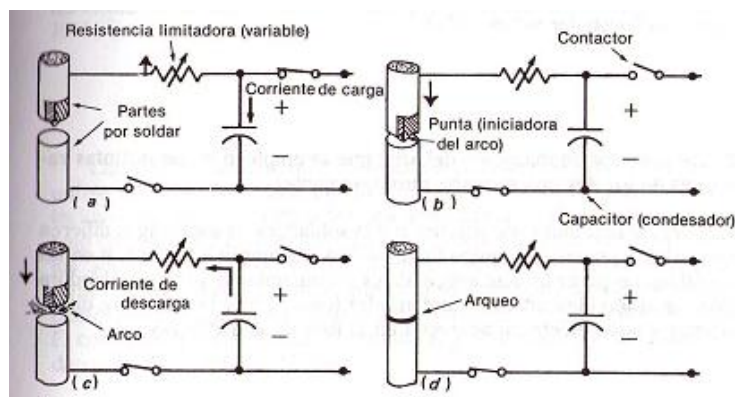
Diagrama simplificado de la secuencia de pasos en la soldadura por percusión con descarga de capacitor: (a) el conector se cierra momentáneamente; (b) se hace avanzar una de las partes por soldar hacia la otra, y se acelera rápidamente; (c) se forma el arco en el entre hierro, poco antes de que se pongan en contacto las partes, y se funden las superficies de trabajo de cada parte explotando el iniciador del arco, si se utiliza; (d) se extingue el arco al forzar el impacto de una parte contra la otra, expulsando el metal fundido en forma de relámpago y presionando las partes hasta quedar en perfecta unión soldada.
